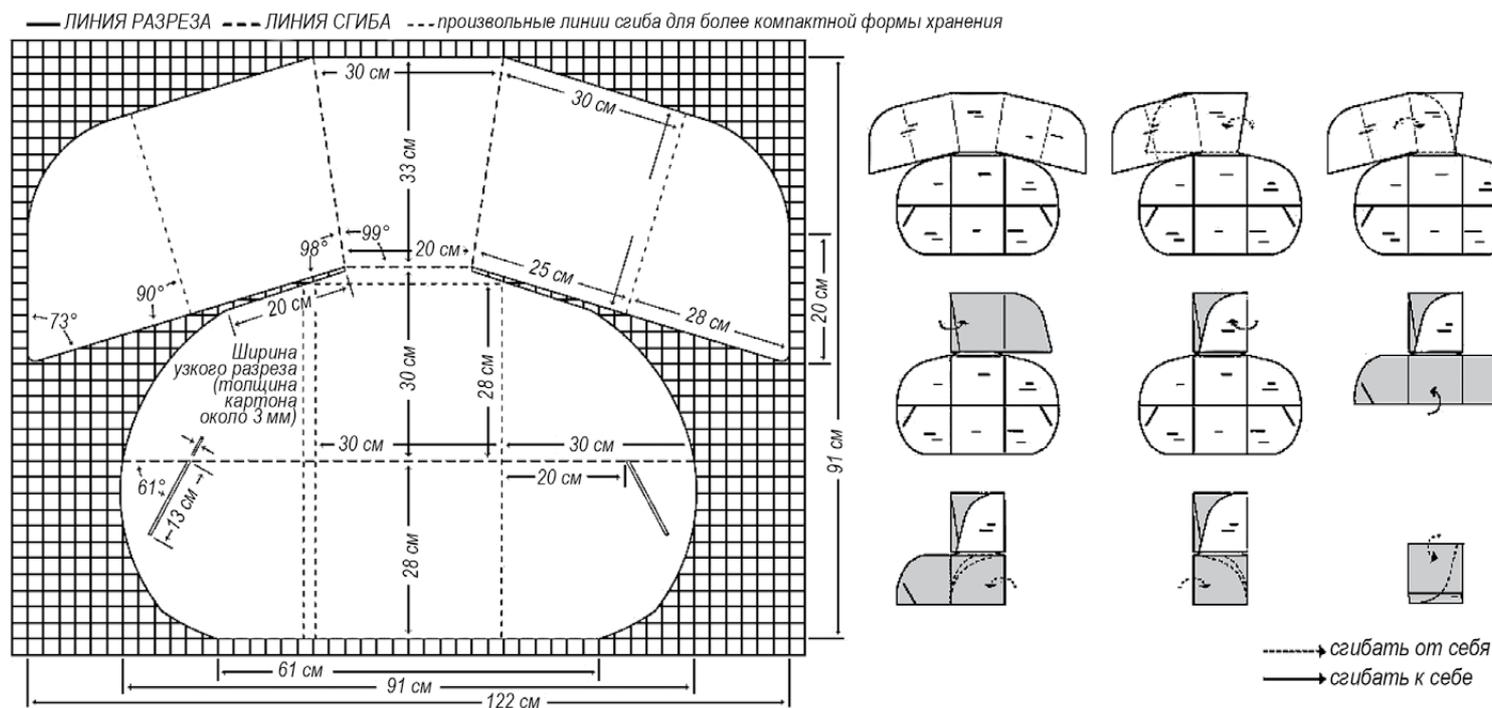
Схема края и сборки отражающей поверхности печи «Кукит»
